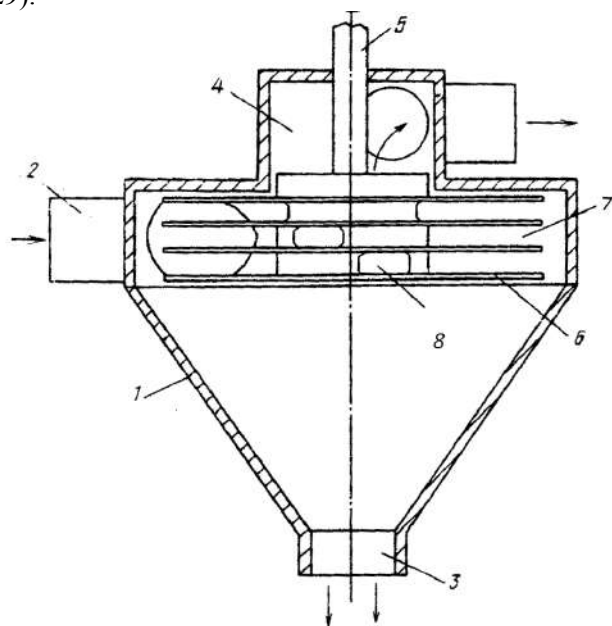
Центробежный классификатор: 1 – корпус; 2 – подача воздуха и исходного материала; 3 – патрубок для вывода крупного продукта; 4 – выход воздуха с мелким продуктом; 5 – вал; 6 – диски; 7 – зона разделения; 8 – отверстия для стока воздуха.
